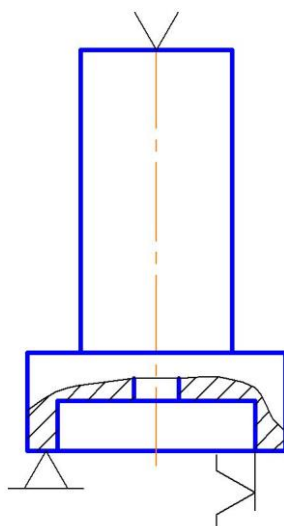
Умовна схема базування при фрезерування зуб'їв на вертикально-фрезерному напівавтоматі
